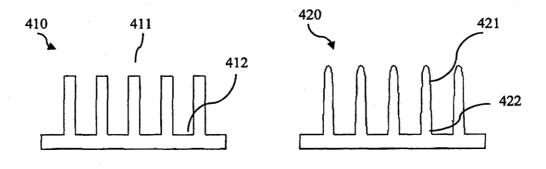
Aletas guía con cima plana FIG. 4.2 Aletas guía con cima redondeada
